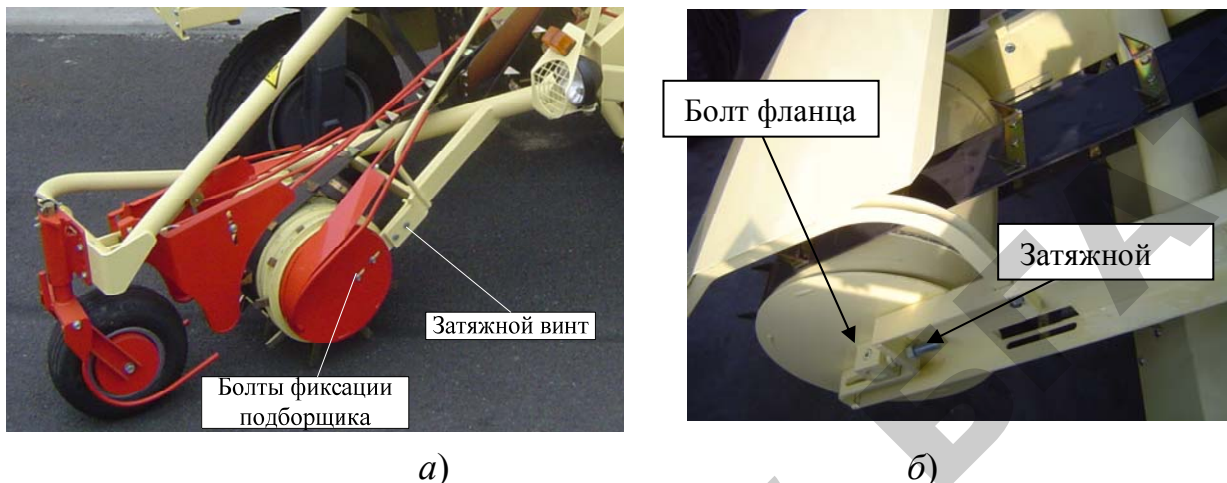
Регулировка натяжения ремней оборачивателя:
